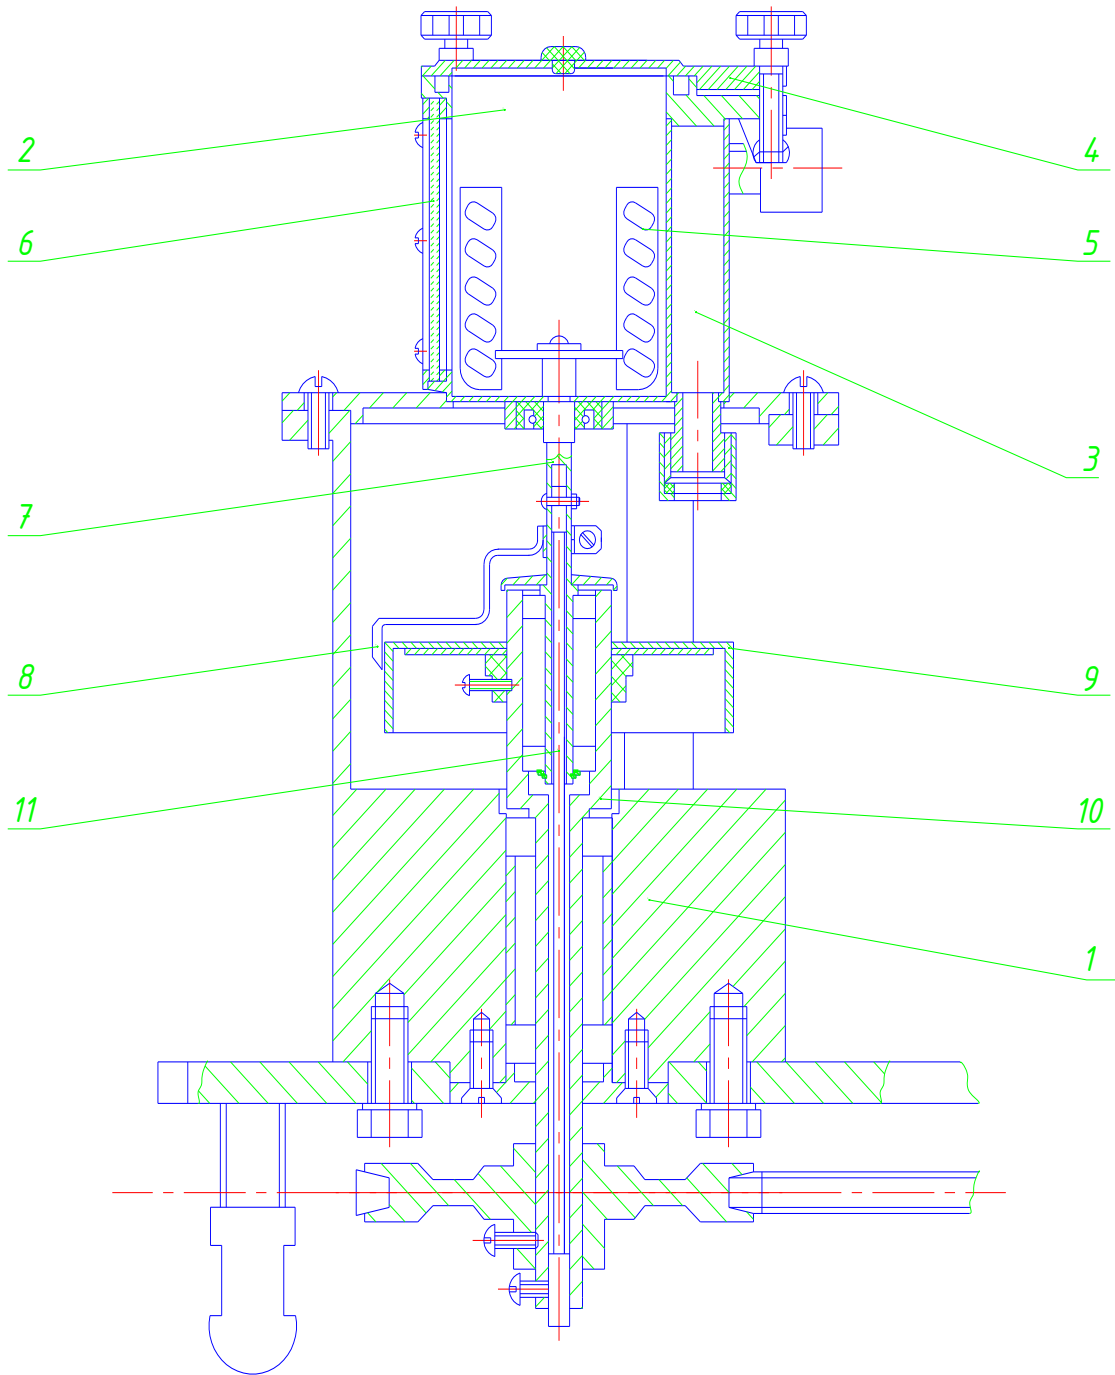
Конструкція лабораторної установки: 1- корпус; 2- колба; 3- сорочка; 4- кришка; 5-мішалка; 6- оглядове скло; 7- ведучий вал; 8- стрілка; 9- диск зі шкалою; 10- проміжний вал; 11-пружний елемент.
